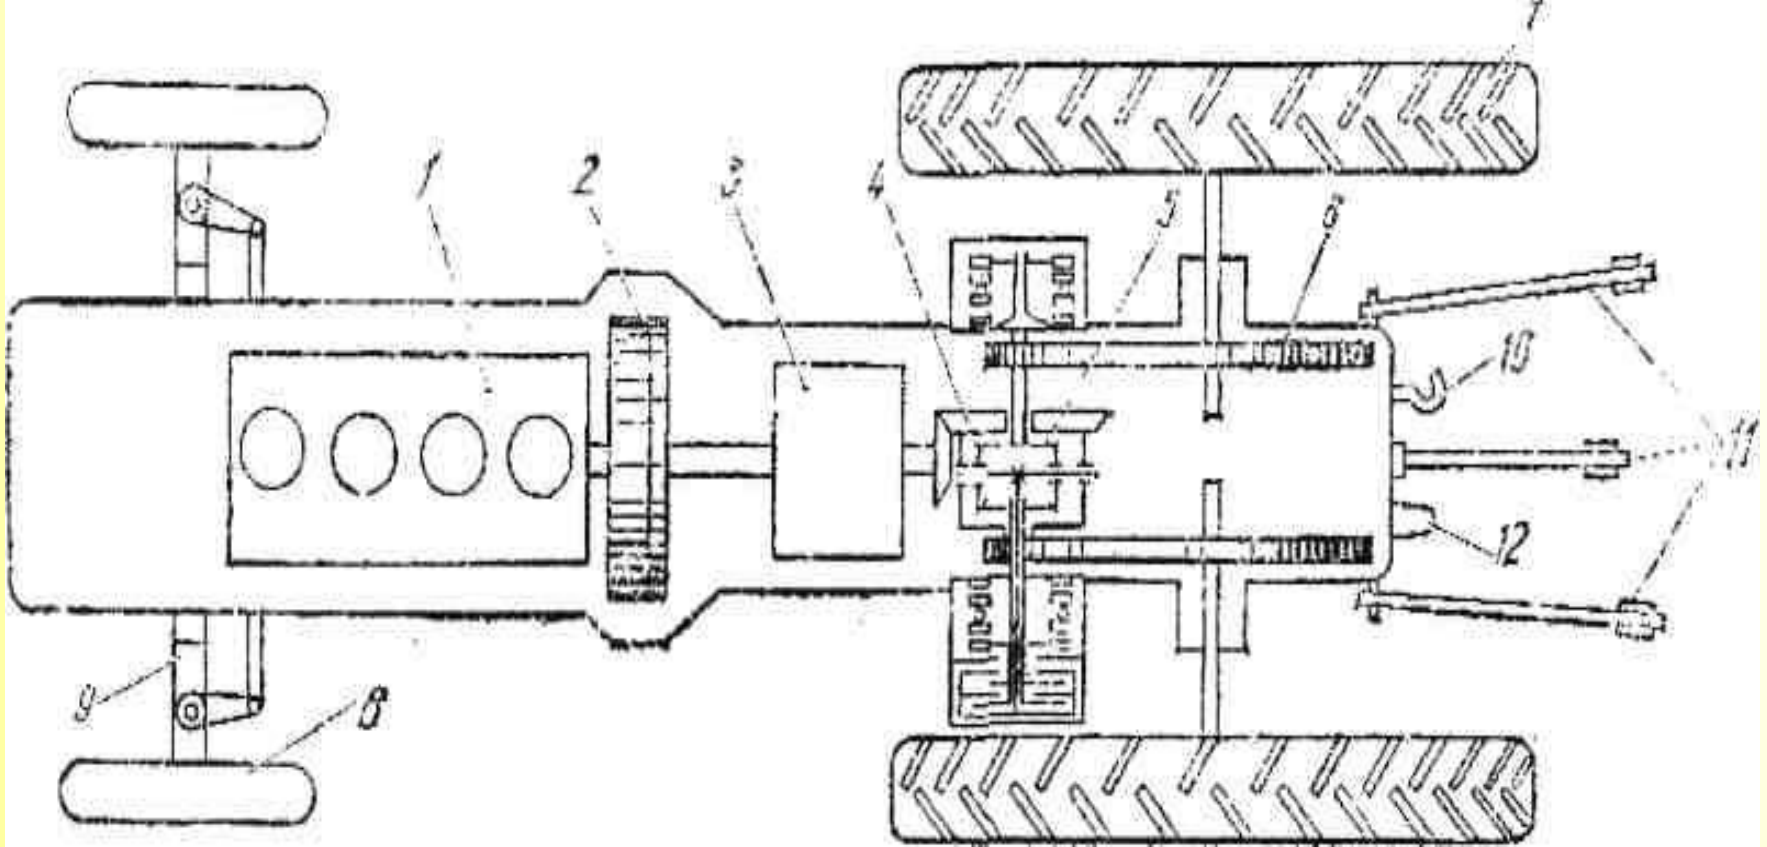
Расположение механизмов и сборочных единиц колесного трактора типа МТЗ-80:
